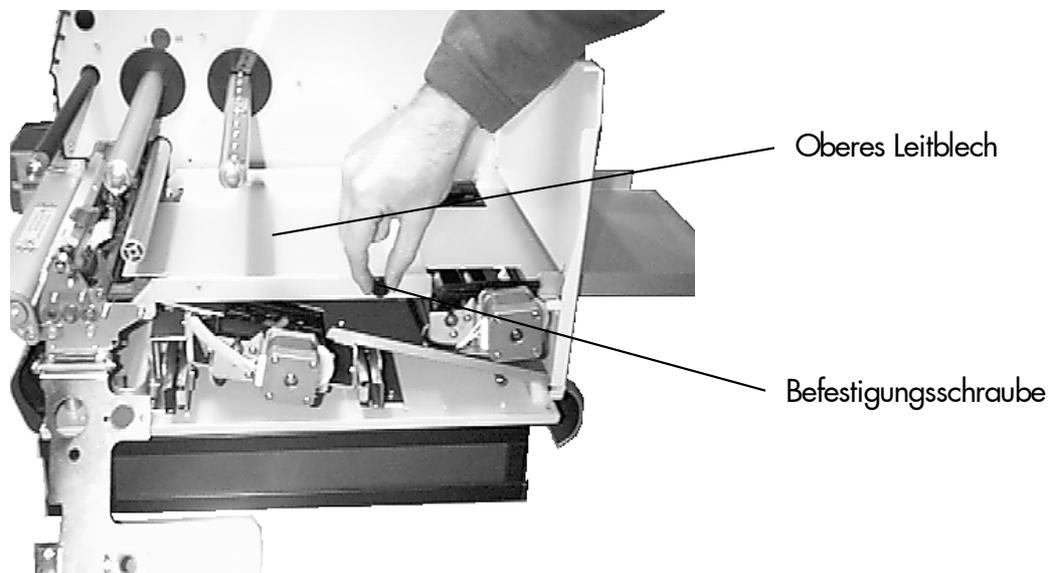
b Befestigungsschraube des oberen Leitbleches lösen
